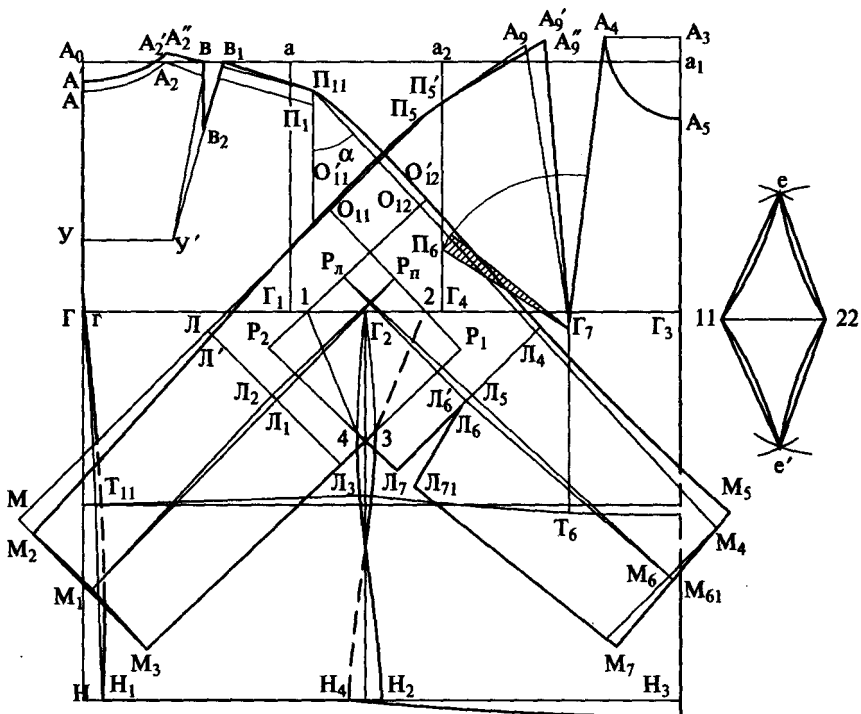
Чертеж конструкции изделия с цельнокроеными рукавами с ромбовидной лапастницей
